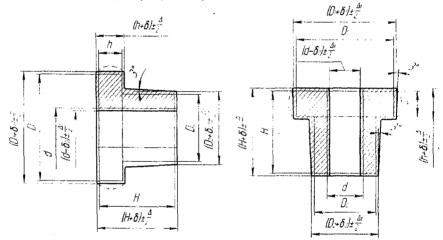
Схема назначения припусков и допусков для поковок 6-ой группы
